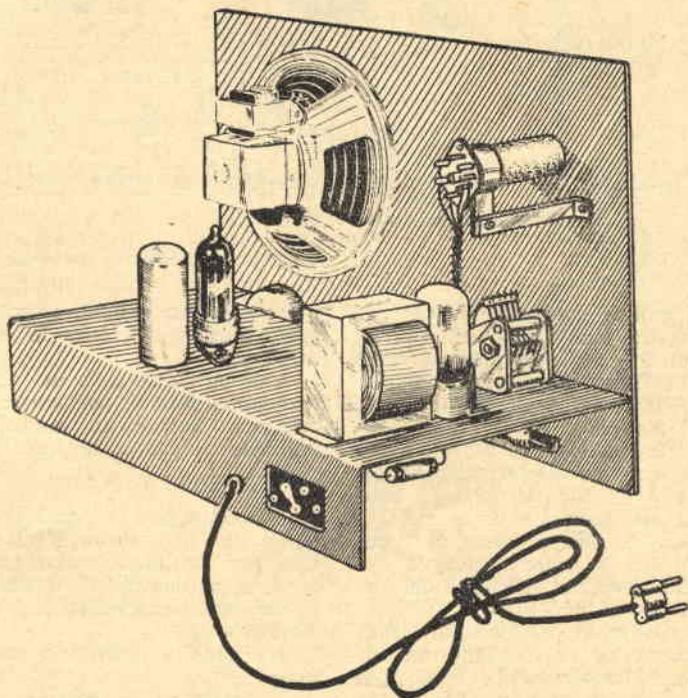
Chassis in alluminio e pannello frontale con componenti montati.
